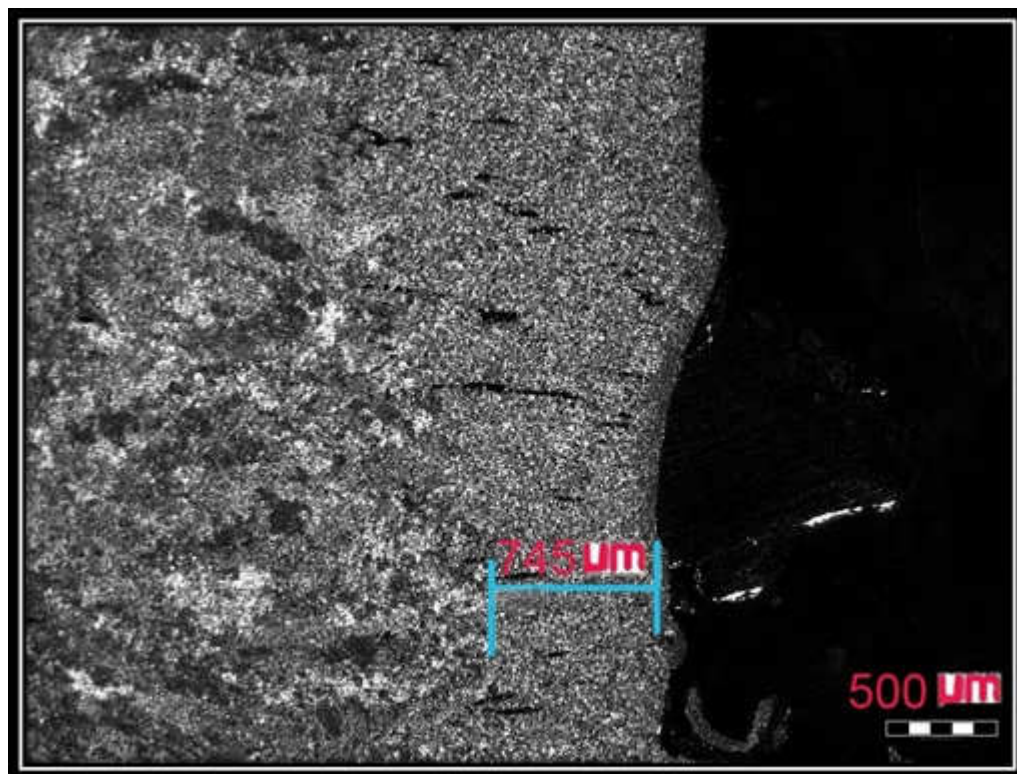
Makrostruktura vzorku 4.3 svařovaného elektrodou ϕ 2,5 mm – termočlánek č. T3
